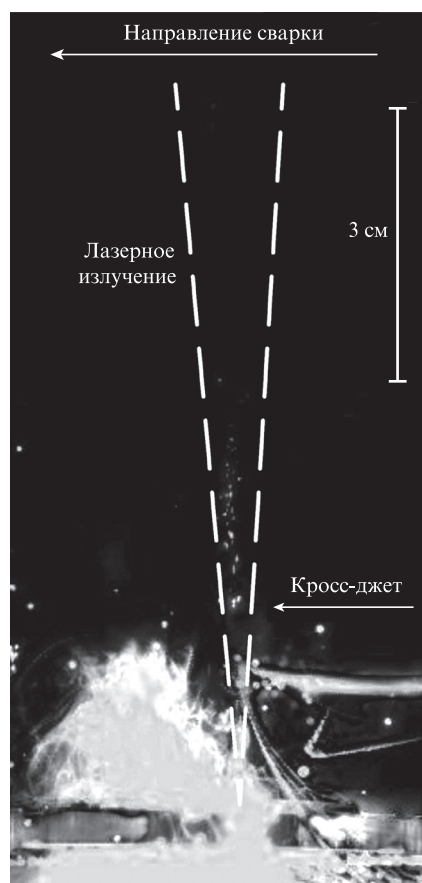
Кадр скоростной видеосъемки сварки титана с использованием кросс-джета сварочного факела сжатым воздухом.
